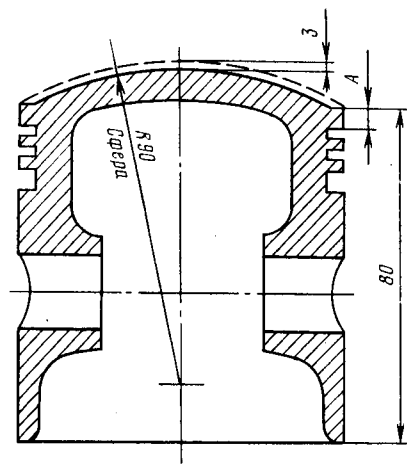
Эскиз обработки поршня двигателя модели 412Э для деформированного двигателя
